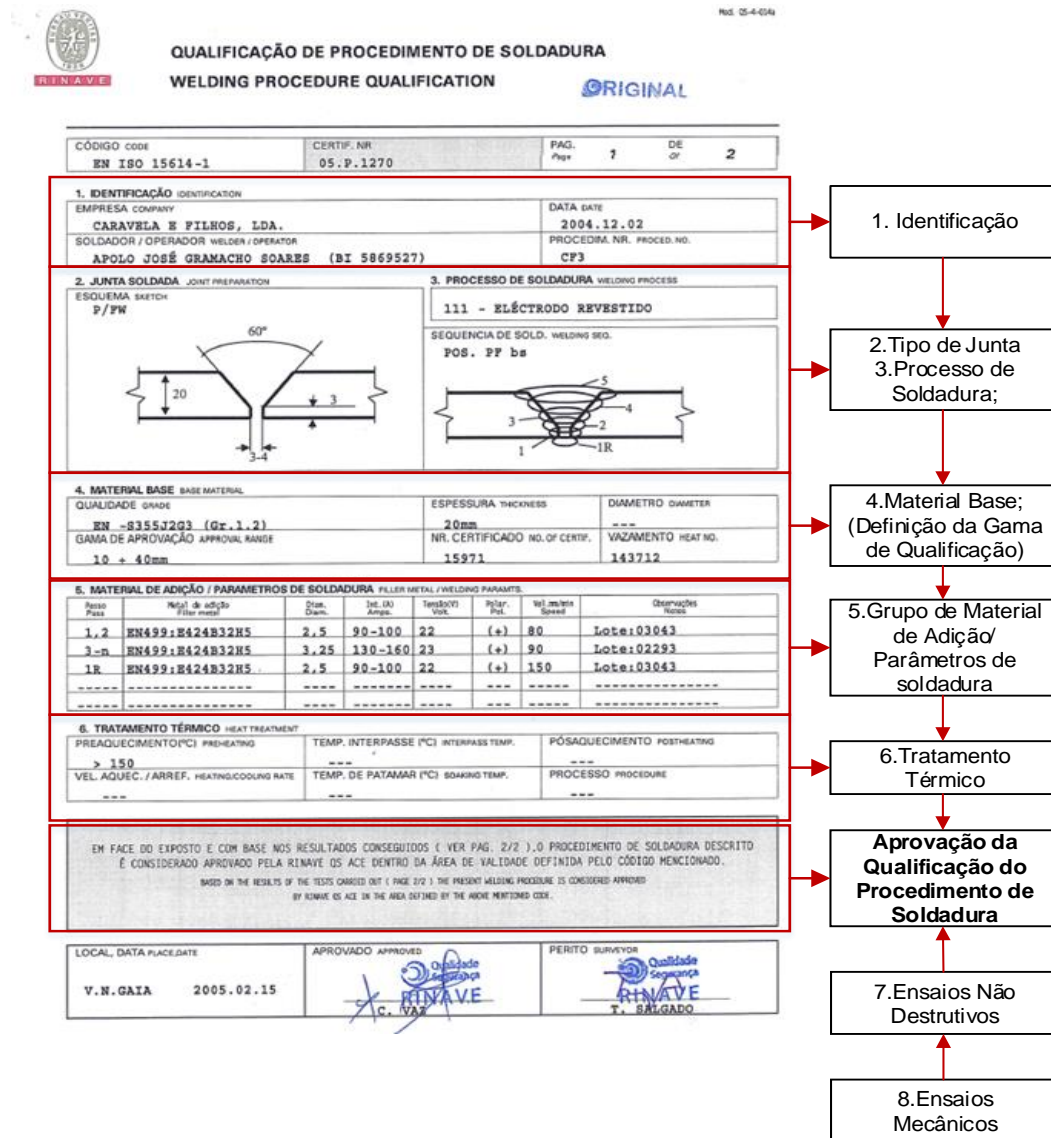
Procedimento de Qualificação de soldadura.
